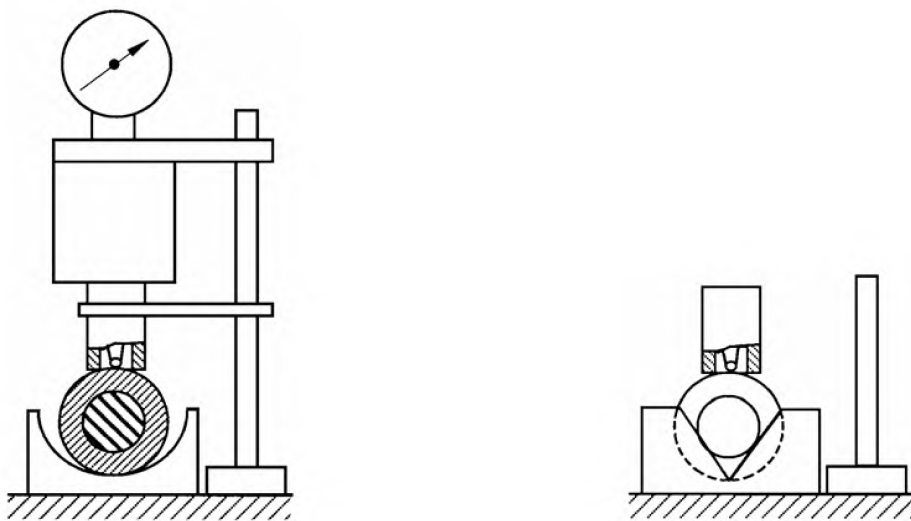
а – Испытуемый образец в направляющей опоре с круглой выемкой
